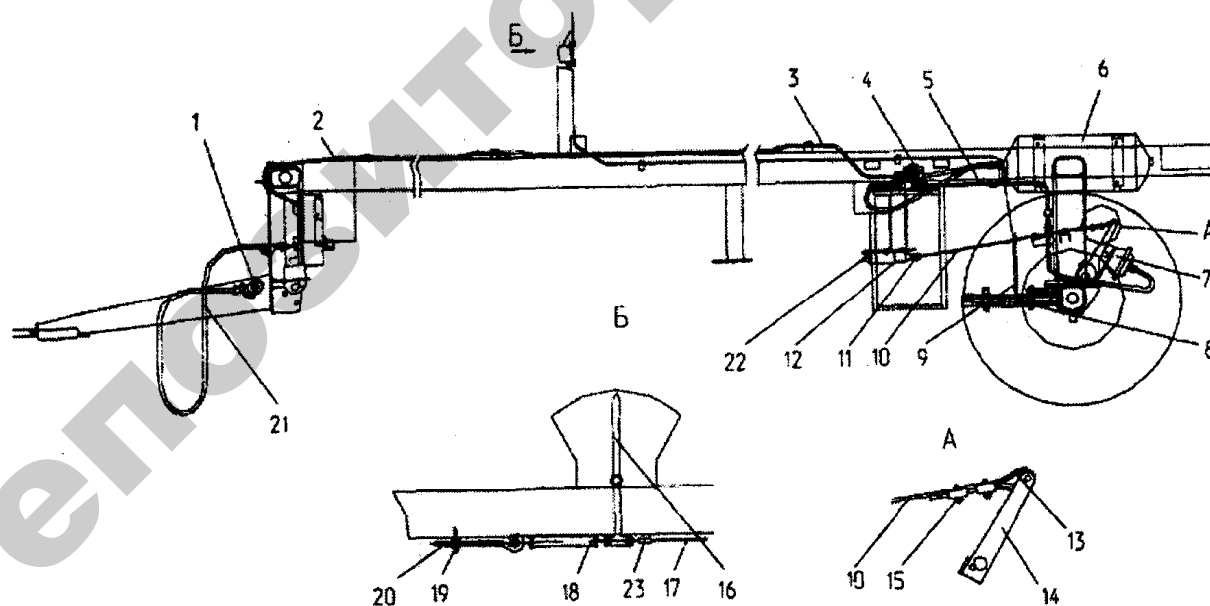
Установка привода тормозов и указателя поворота колес:
